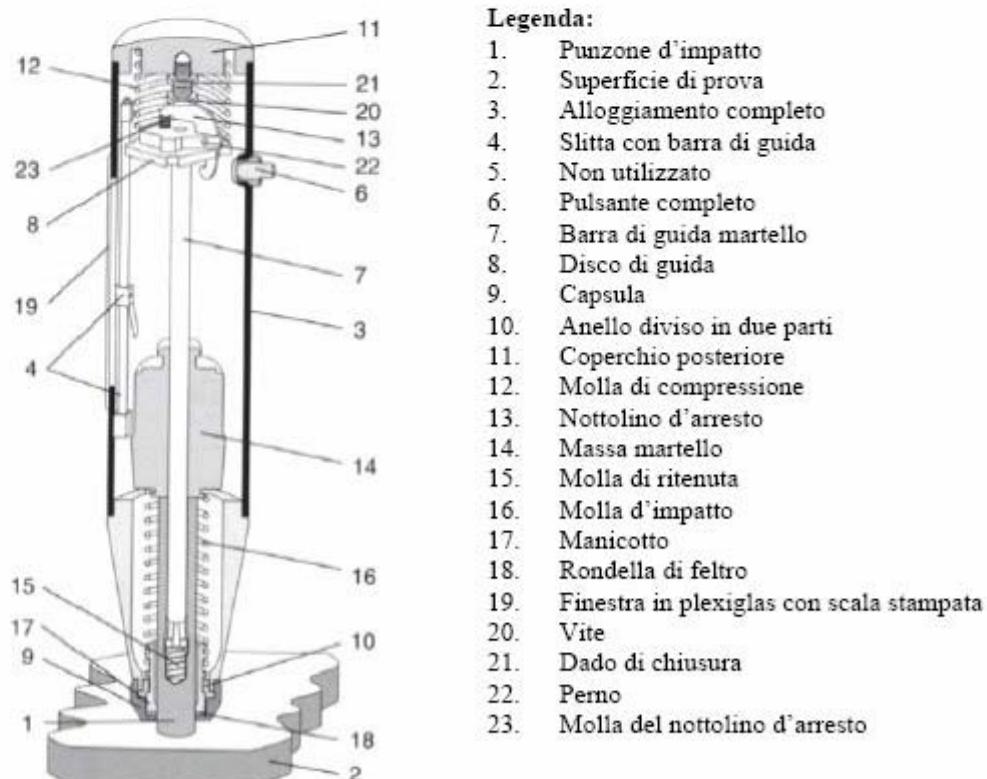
Sezione longitudinale dello sclerometro di calcestruzzo
